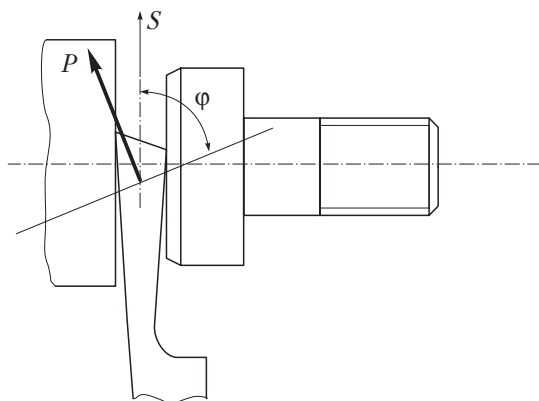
Схема отрезания детали от групповой заготовки резцом с углом в плане $\varphi < 90^\circ$
